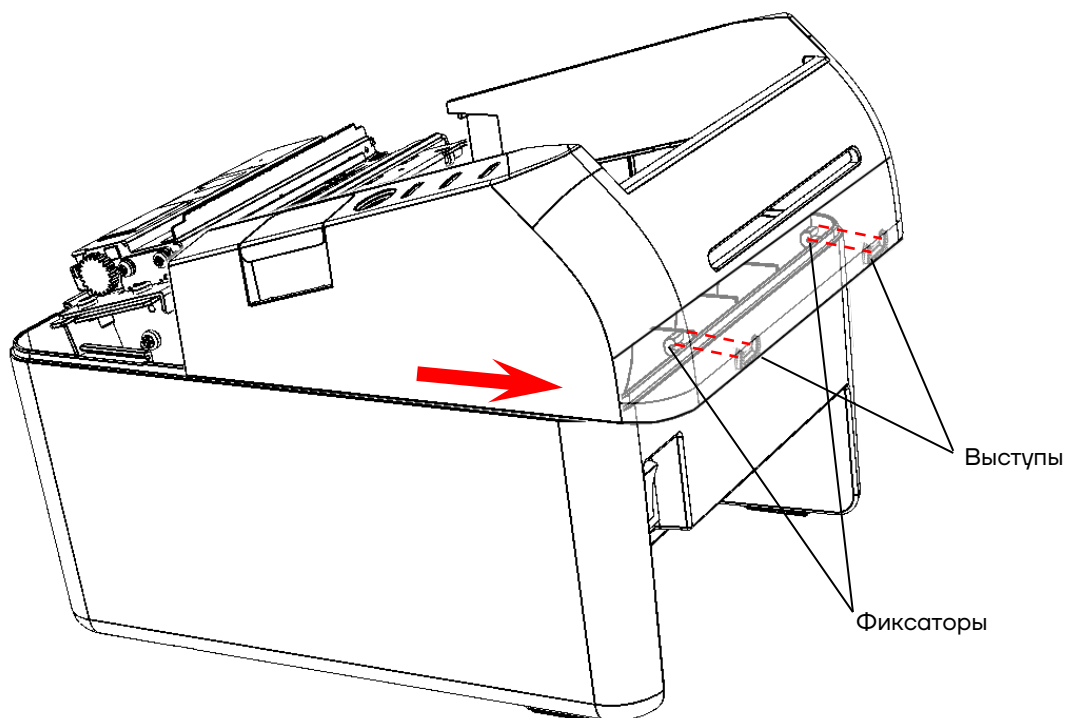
Смещение верхней части корпуса (задние фиксаторы)
